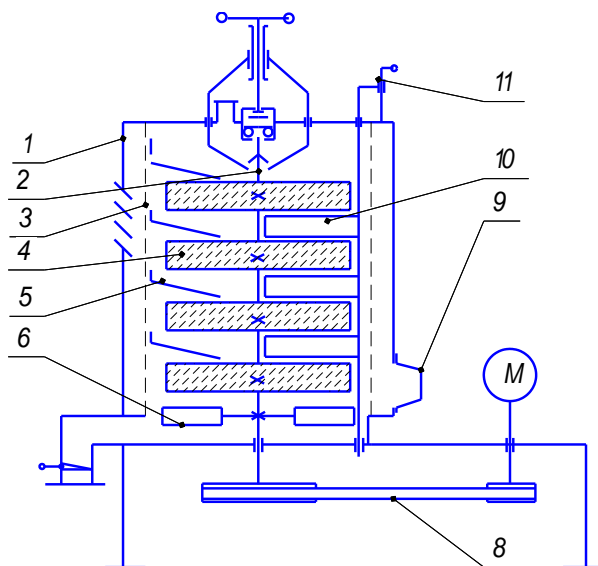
Машина луцильна 1 - корпус; 2-вал; 3-сітка; 4-диск; 5-скат; 6-крильчатка; 7,11,12-регуля-тори; 8-привід; 9-патрубок повітряний; 10-пластина направляюча.
